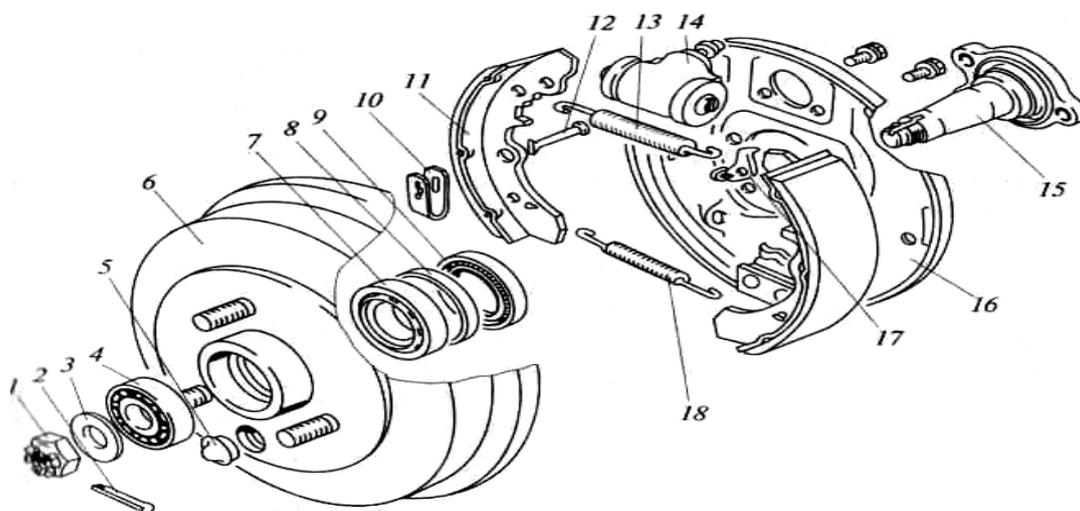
Детали тормозного механизма с барабанными тормозами и оси заднего колеса: 1- гайка; 2 — шплинт; 3 — шайба; 4 — рычаг привода; 5 — заглушка; 6-барабан со ступицей колеса; 7— задний подшипник; 8 — дистанционное кольцо сальника; 9 — сальник; 10 — пластинчатая пружина; 11 — тормозная колодка; стойка колодки; 13 — толкатель; 14 — колесный цилиндр; 15 — тяга привода; 16 — тормозной щит; 17 — зацеп пружины; 18 — нижняя стяжная пружина колодок.
